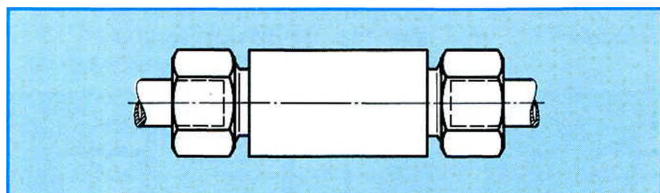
Резьбовое соединение через переборку, с концами под сварку
